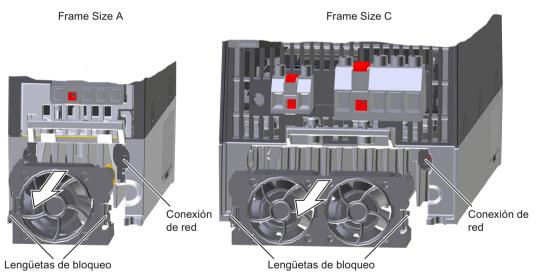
Desmontaje de la unidad de ventilador del disipador
